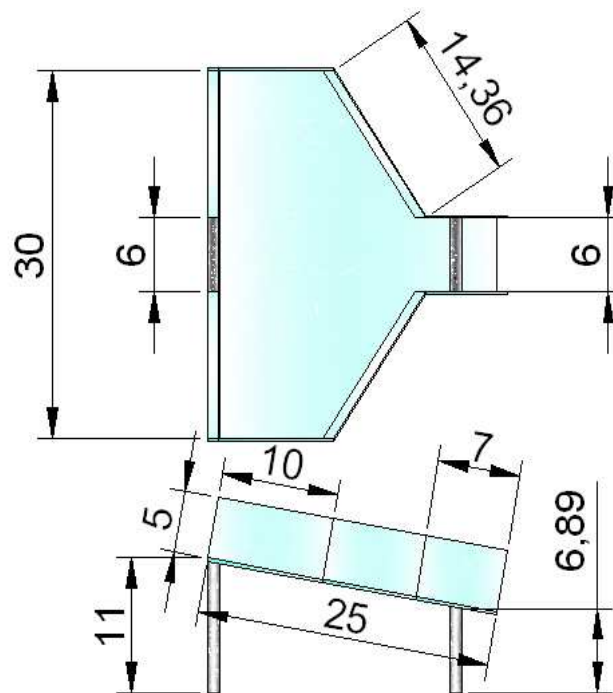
Diseño de la tolva receptora con dimensiones en centímetros.
